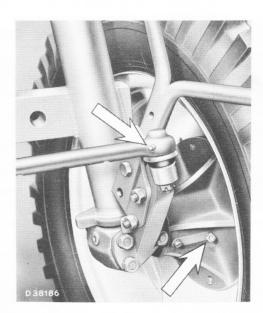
Points de graissage du moyeu de roue avant et de la barre d'accouplement
